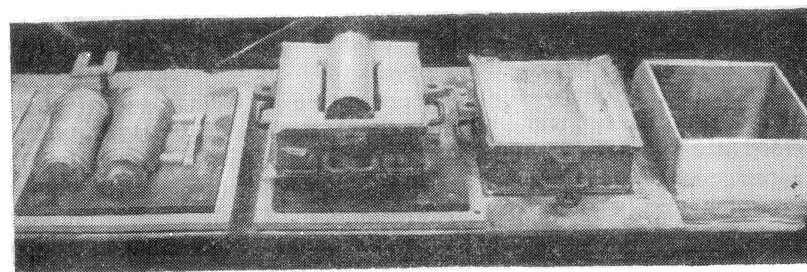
Форма из сыпучих песков и порошков перед сборкой.
